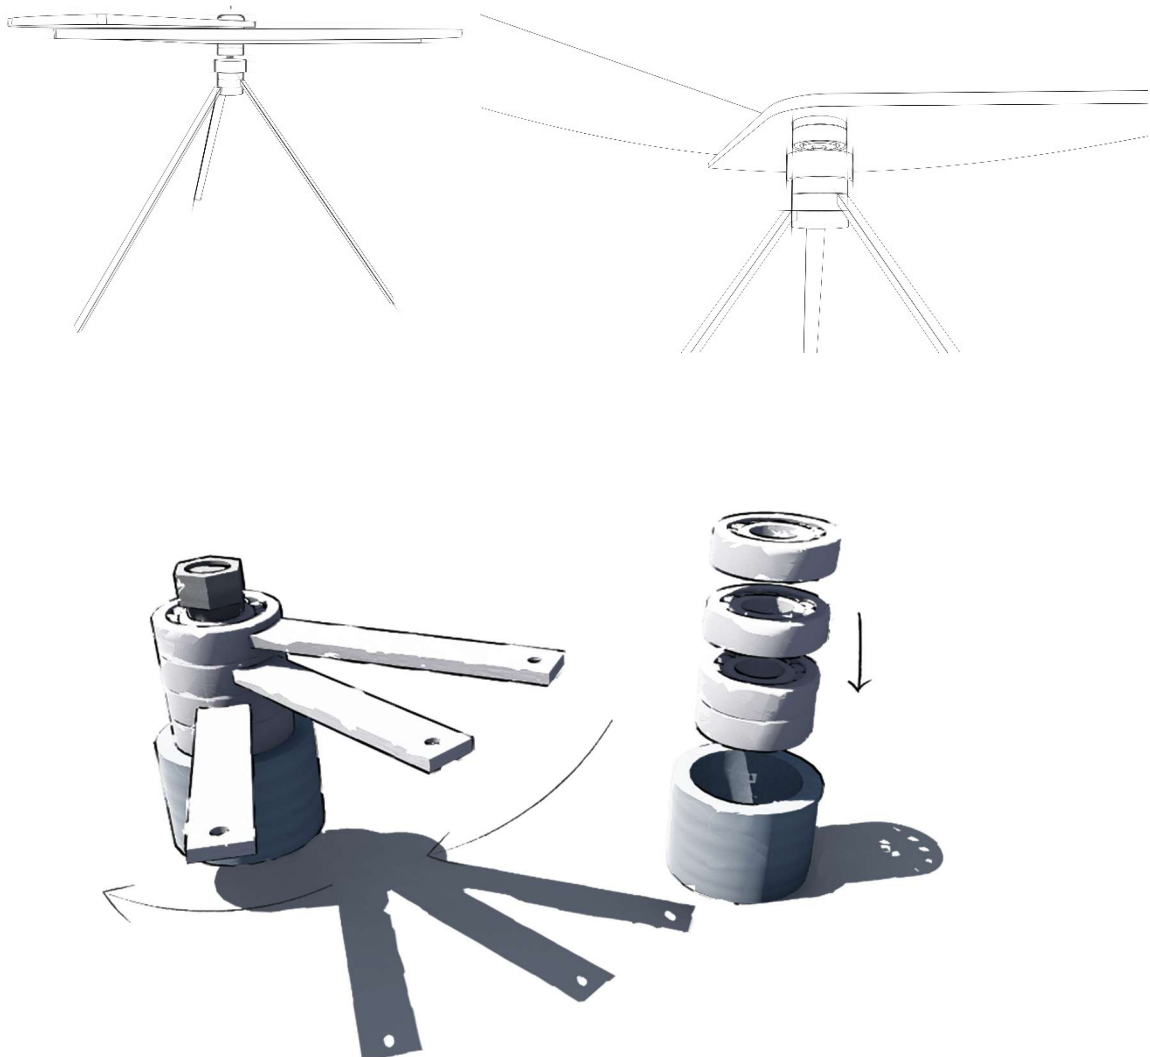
Sketch mecanismo 2 – Mecanismo Vista Explodida
